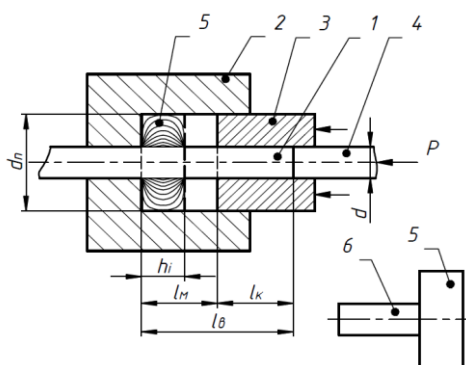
Схема штамповки стержневых изделий [3]: 1- заготовка; 2- матрица; 3 – направляющая втулка; 4 – пуансон; 5- формируемое утолщение 6 – изделие.
